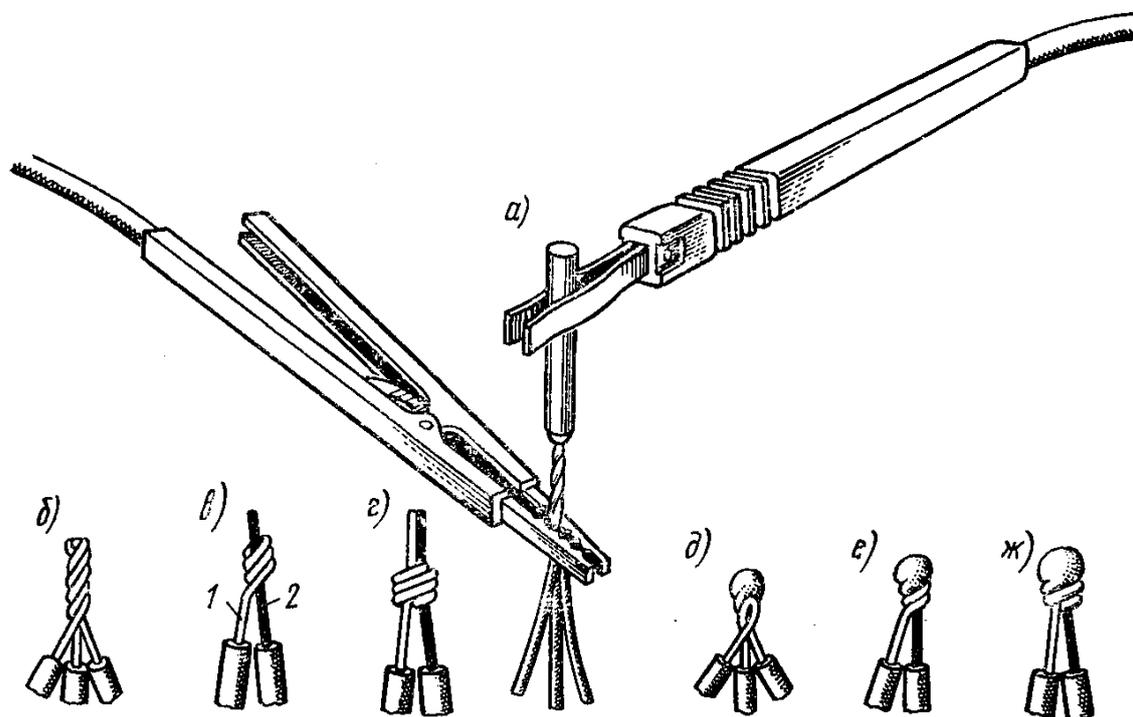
Сварка жил угольным электродом: а - сварка; б - алюминиевые жилы, подготовленные к соединению; в, г - алюминиевая и медная жилы, подготовленные к соединению; д - сварное соединение алюминиевых жил; е, ж - сварное соединение алюминиевой жилы с медной; 1 - алюминиевая жила; 2 - медная жила
